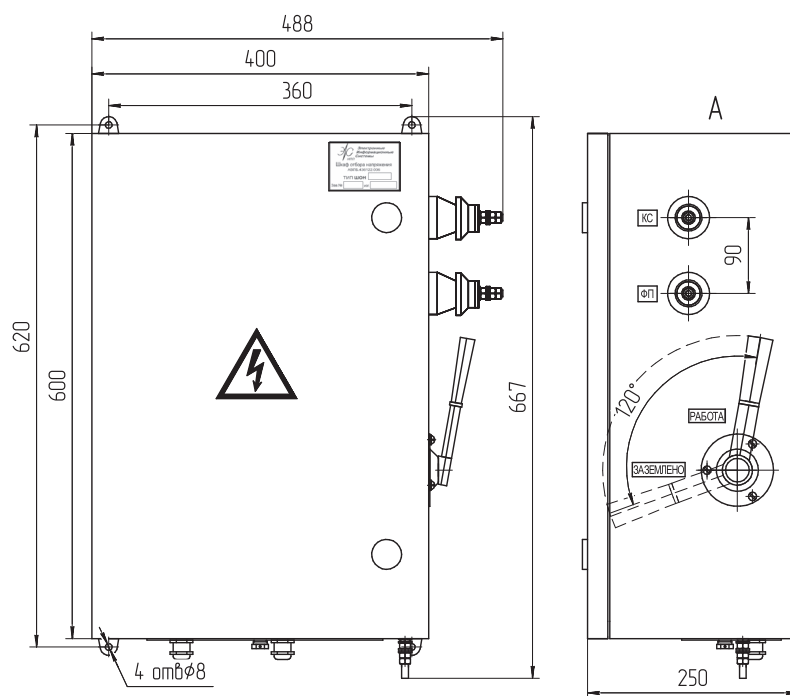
Габаритно-присоединительный чертеж ШОН-303П.
